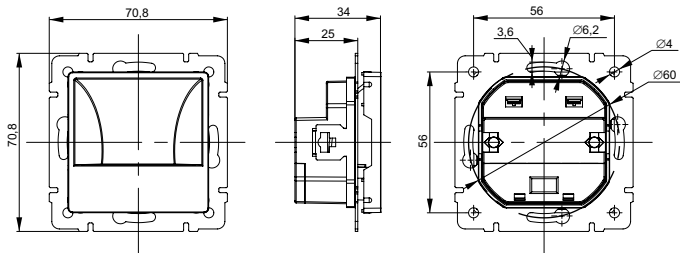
Габаритные размеры подсветки / Figure 2 – Overall dimensions of the illumination /
